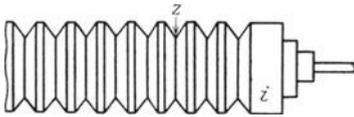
Brennzylinder der Chenilleschneidmaschine.
